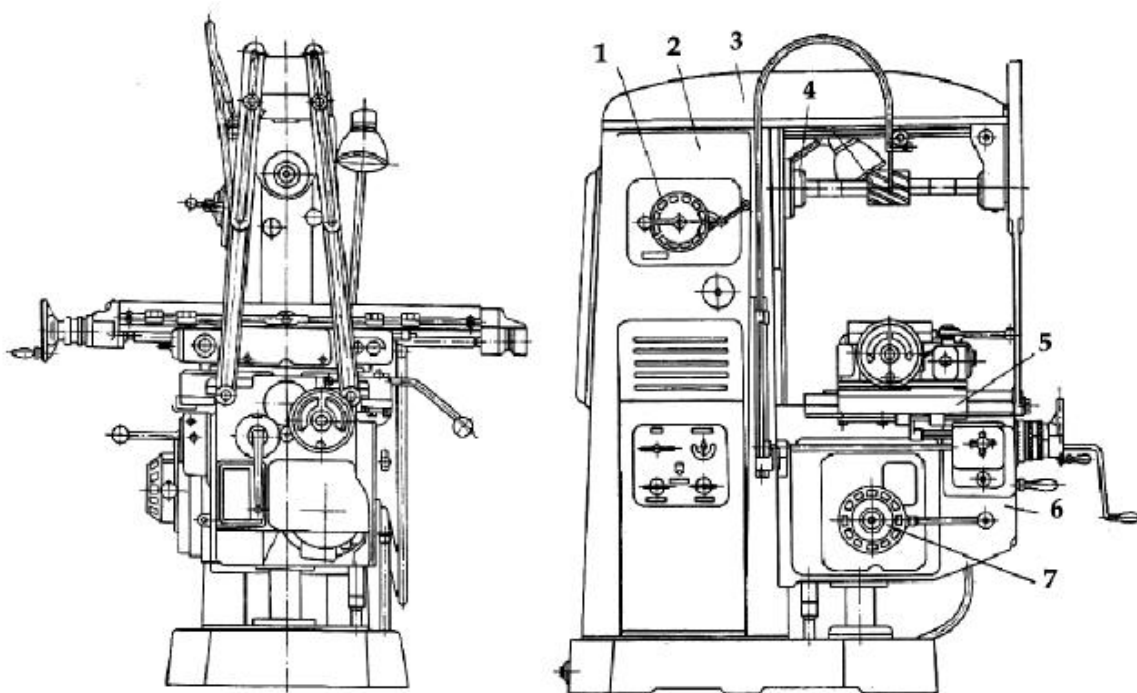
Горизонтально-фрезерний верстат: 1 – коробка швидкостей; 2 – станина; 3 – хобот; 4 – шпиндель; 5 – стол; 6 – консоль; 7 – коробка подач
